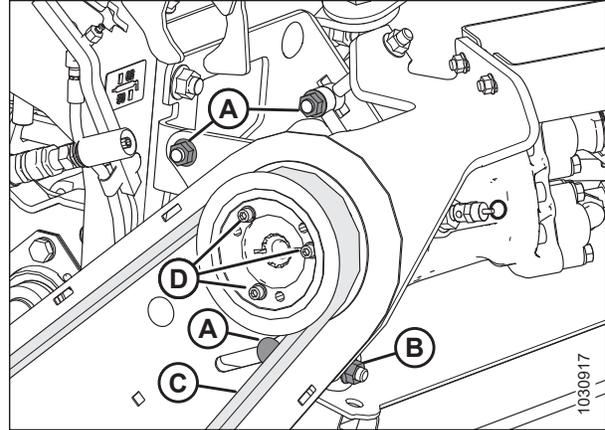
Ведущий шкив — Гидромотор привода плющилки
